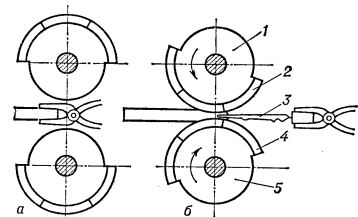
Схема вальцевания: а — исходное положение; б — рабочее положение; 1, 5 — валки; 2, 4 — штампы (секторы); 3 — заготовка.
